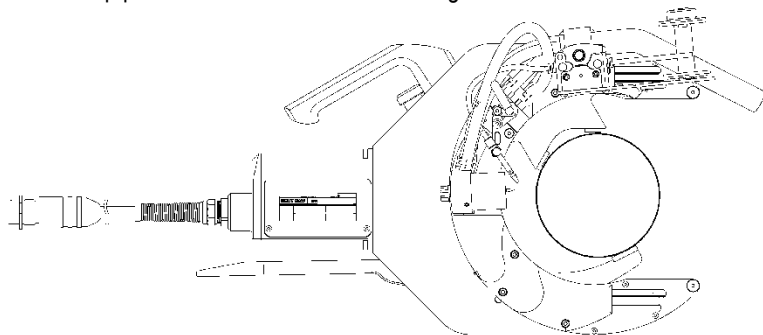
Platzierung des Schweißkopfes
